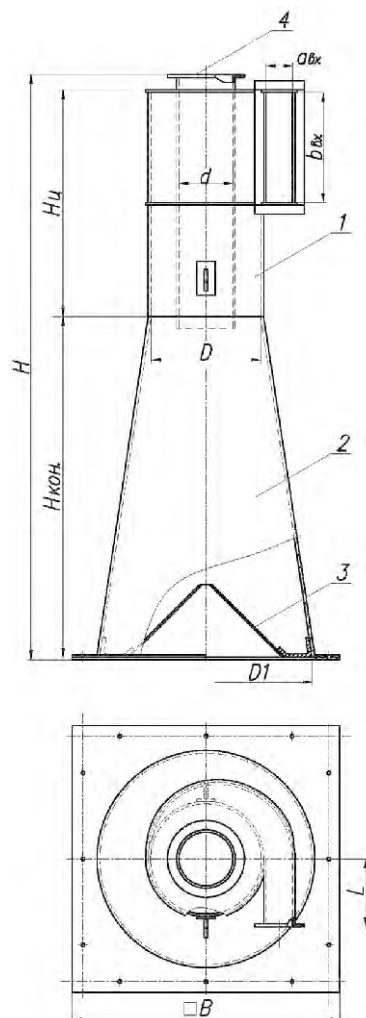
Габаритные и присоединительные размеры циклонов ЦОК.
